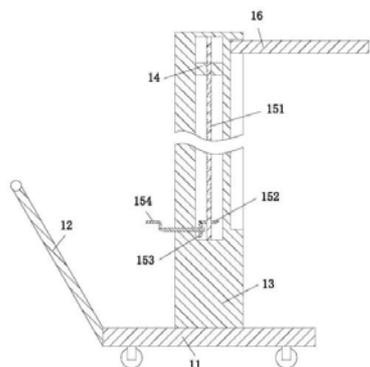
是水利工程基坑管井填埋施工方法的主剖视平面结构示意图
